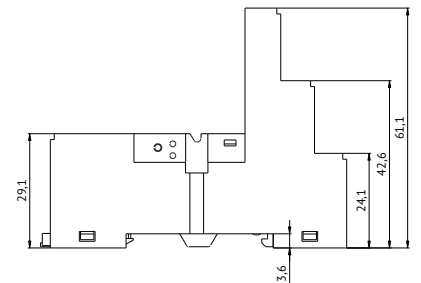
Габаритные, установочные, присоединительные размеры розеток OptiRel G RR94-9X
